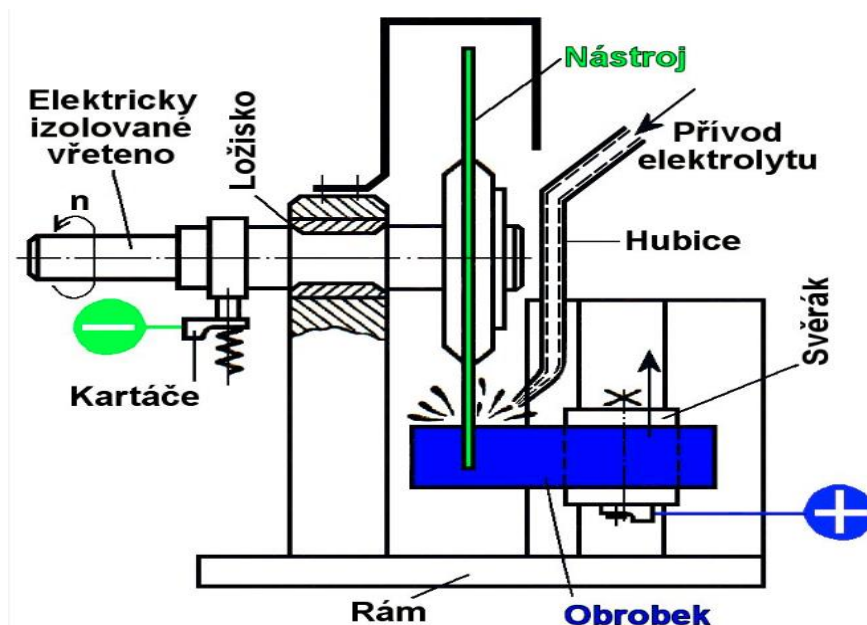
Princip stroje pro elektrokontaktní dělení materiálů (ŘASA a kol., 2001)
